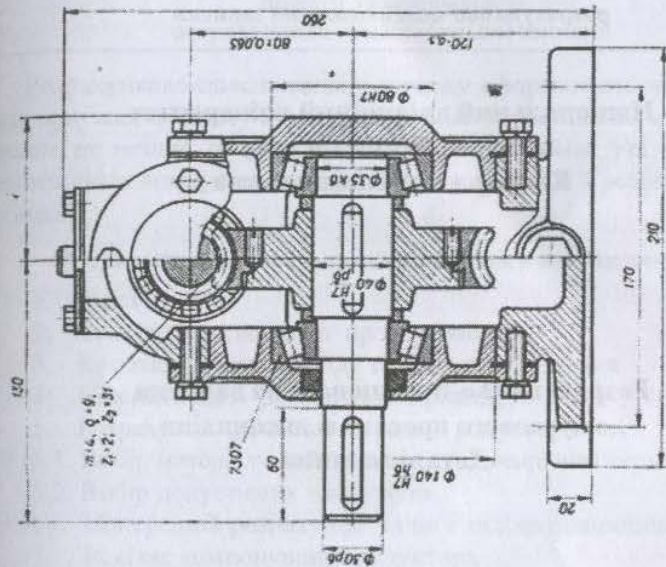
Редуктор черв'ячний з верхнім розміщенням черв'яка
